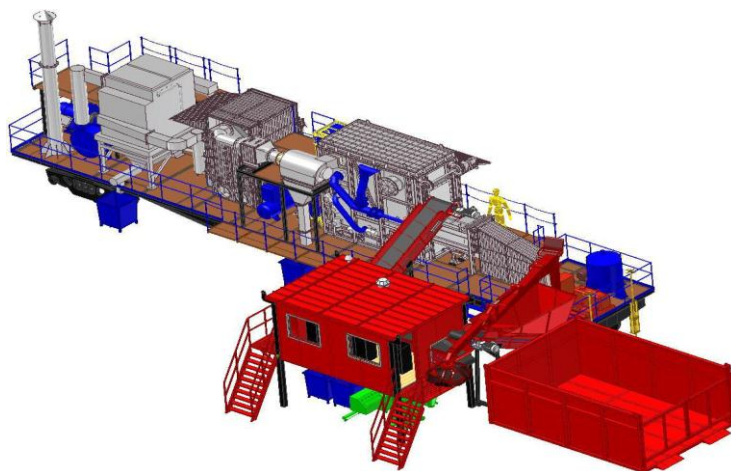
Общий вид мобильного мусороперерабатывающего комплекса МПК-300
